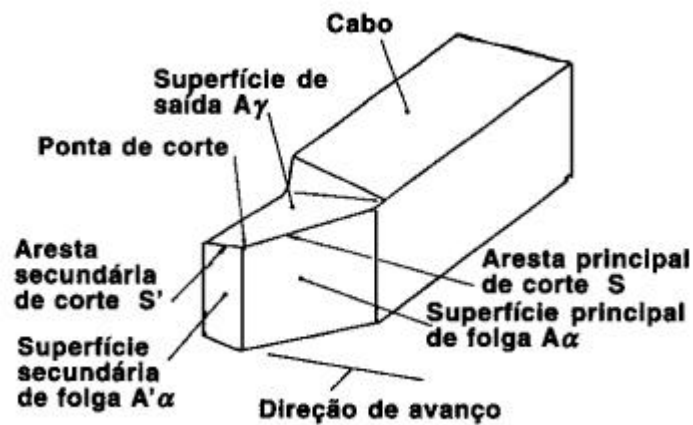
Geometria da ferramenta de corte (Fonte: Machado e Silva, 1999).
